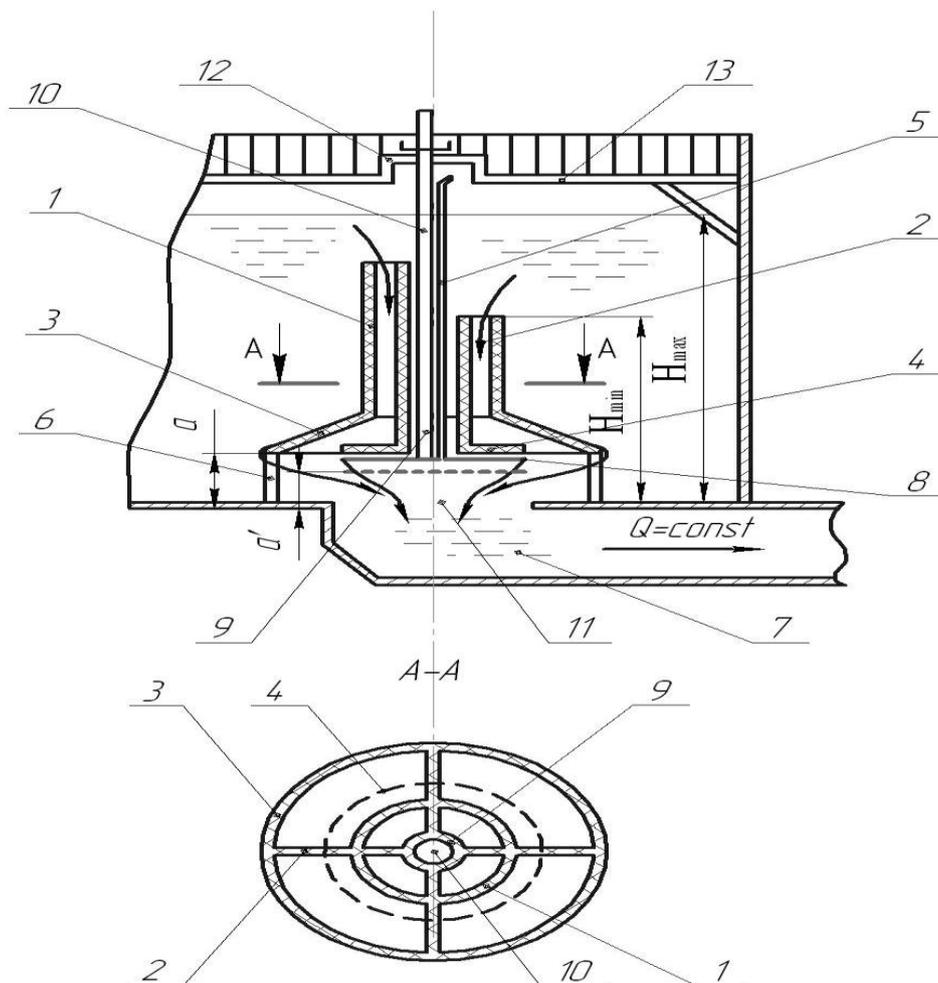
Коробчатый моноблочный стабилизатор с подвижным дисковым клапаном
